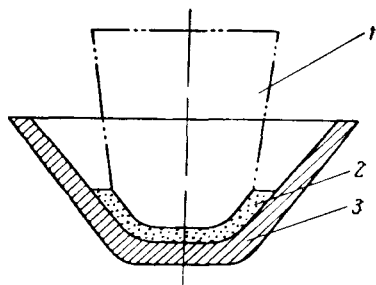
Изготовление жидкой шлаковой формы для приема металла:
